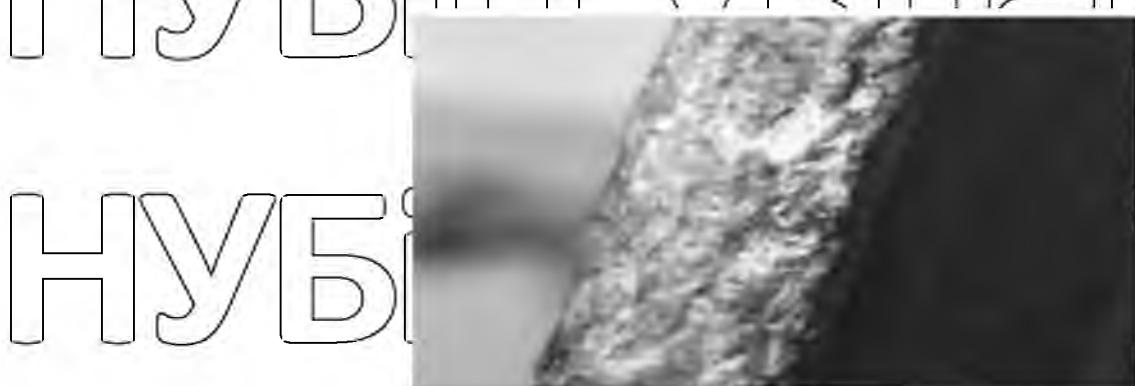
Зношена поверхня зварювального ролика установки 011-1-
